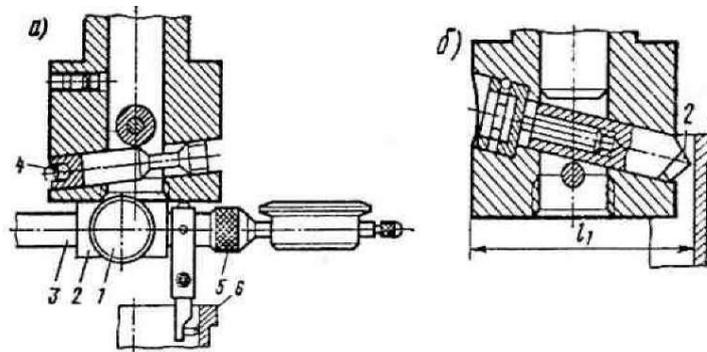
Різцева головка верстата 2А78Н с пристосуваннями для центрування гільз (а) і установки різця (б)
